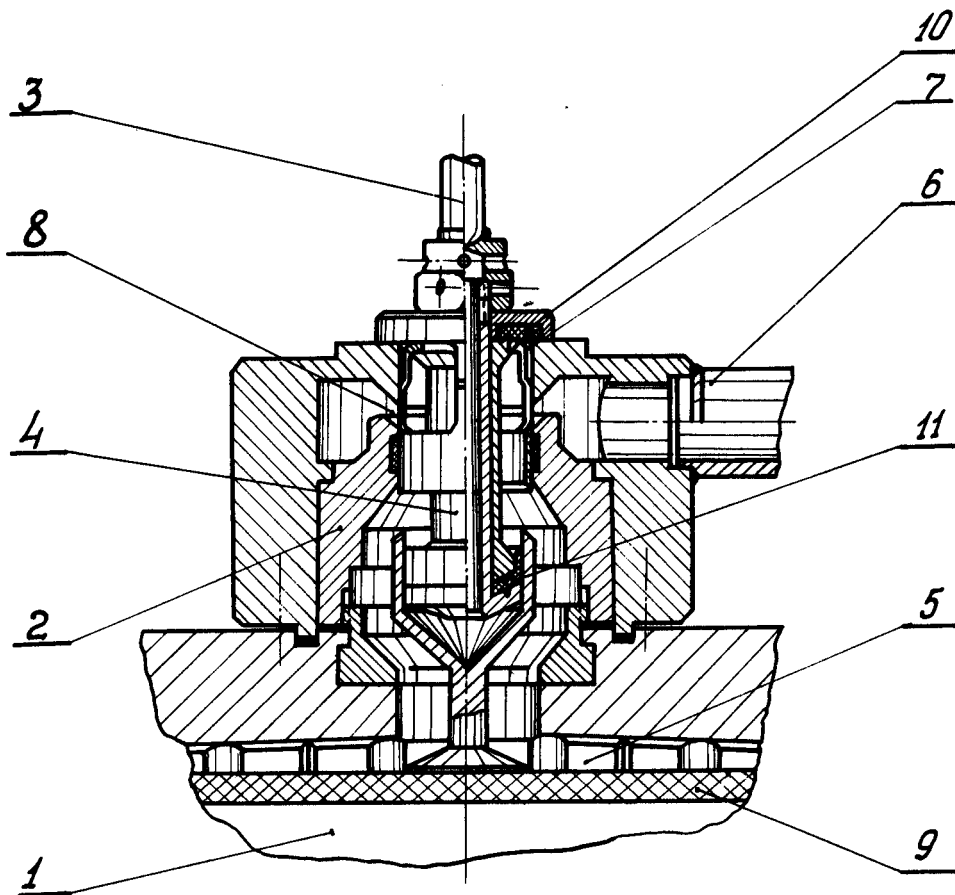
Пневматический усилитель. 1 - пневматический клапан; 2 - корпус; 3 - шток привода; 4 - золотник; 5 - объем управляющего давления; 6 - напорный штуцер; 7 - отверстие выхлопа; 8 - щель для подачи управляющего давления; 9 - затвор пневмоклапана; 10 - уплотнение золотника (верхнее); 11 - уплотнение золотника (нижнее).
